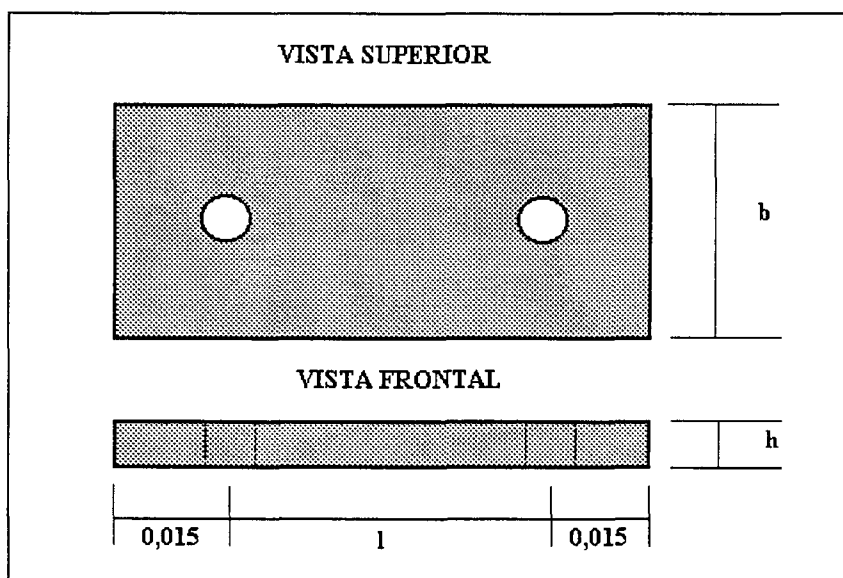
Desenho esquemático do dimensional das molas de flexão.
